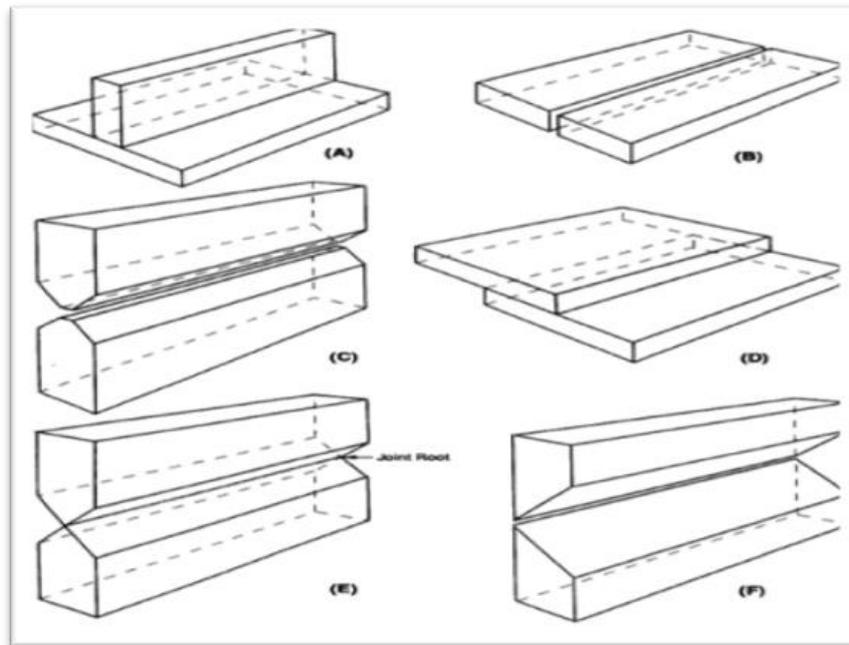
Tipos de preparación de juntas para soldadura
